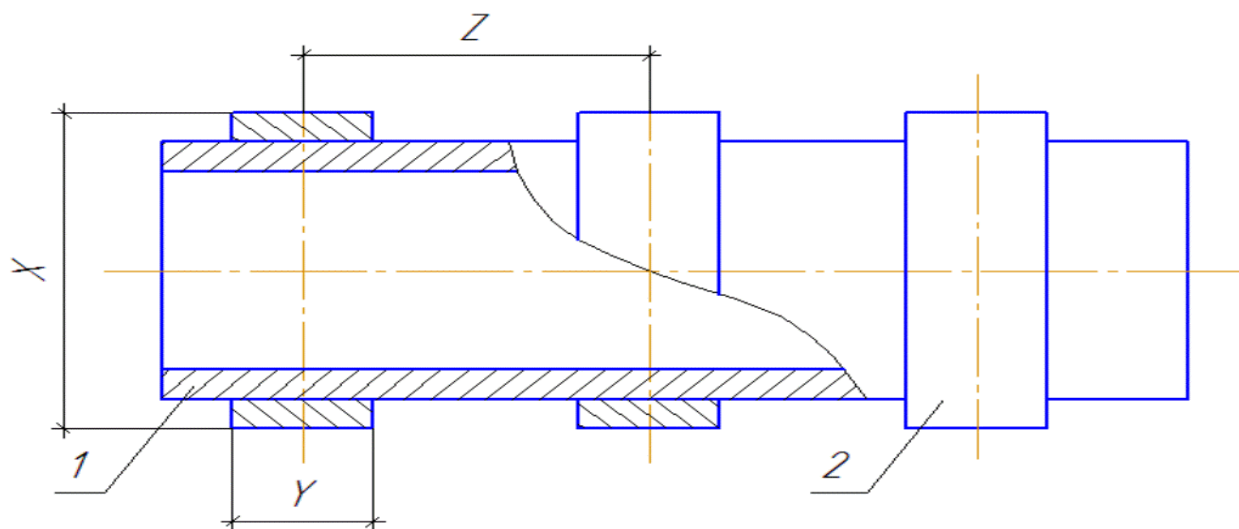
Способ изготовления гидравлических цилиндров
